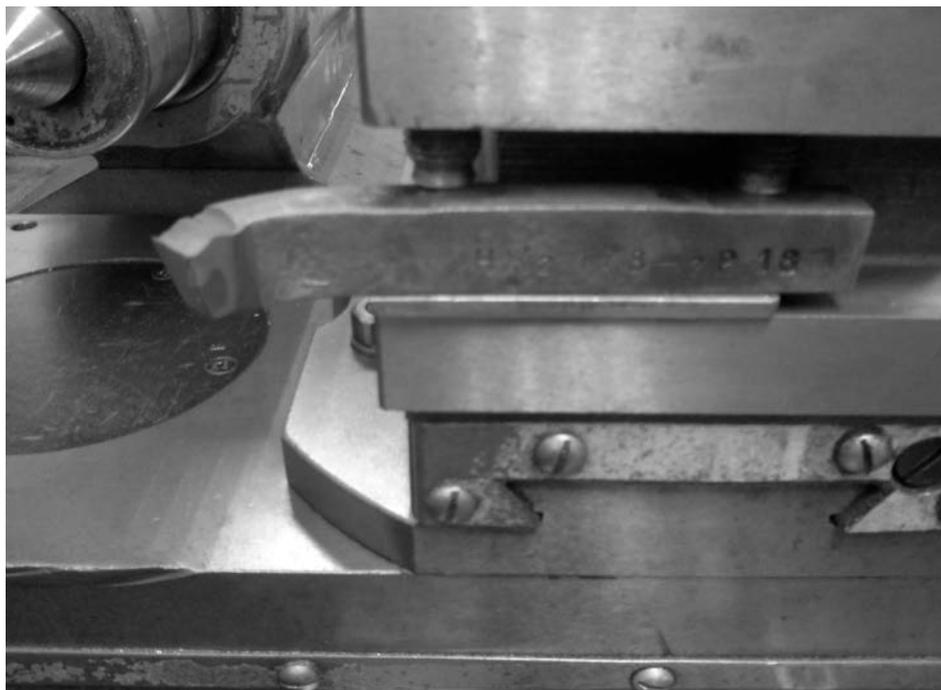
Резец P18 в резцедержателе станка (выполнено авторами)
